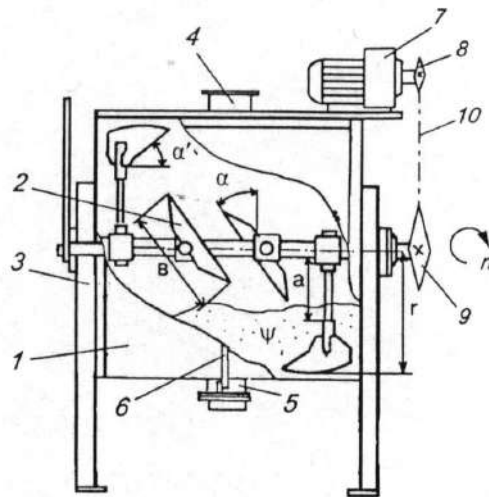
Схема экспериментальной установки. 1- корпус смесителя; 2- мешалка; 3- рама; 4- загрузочный патрубок; 5- разгрузочный элемент; 6- задвижка; 7- электропривод; 8- звездочка; 9- тензозвездочка; 10- цепная передача.
